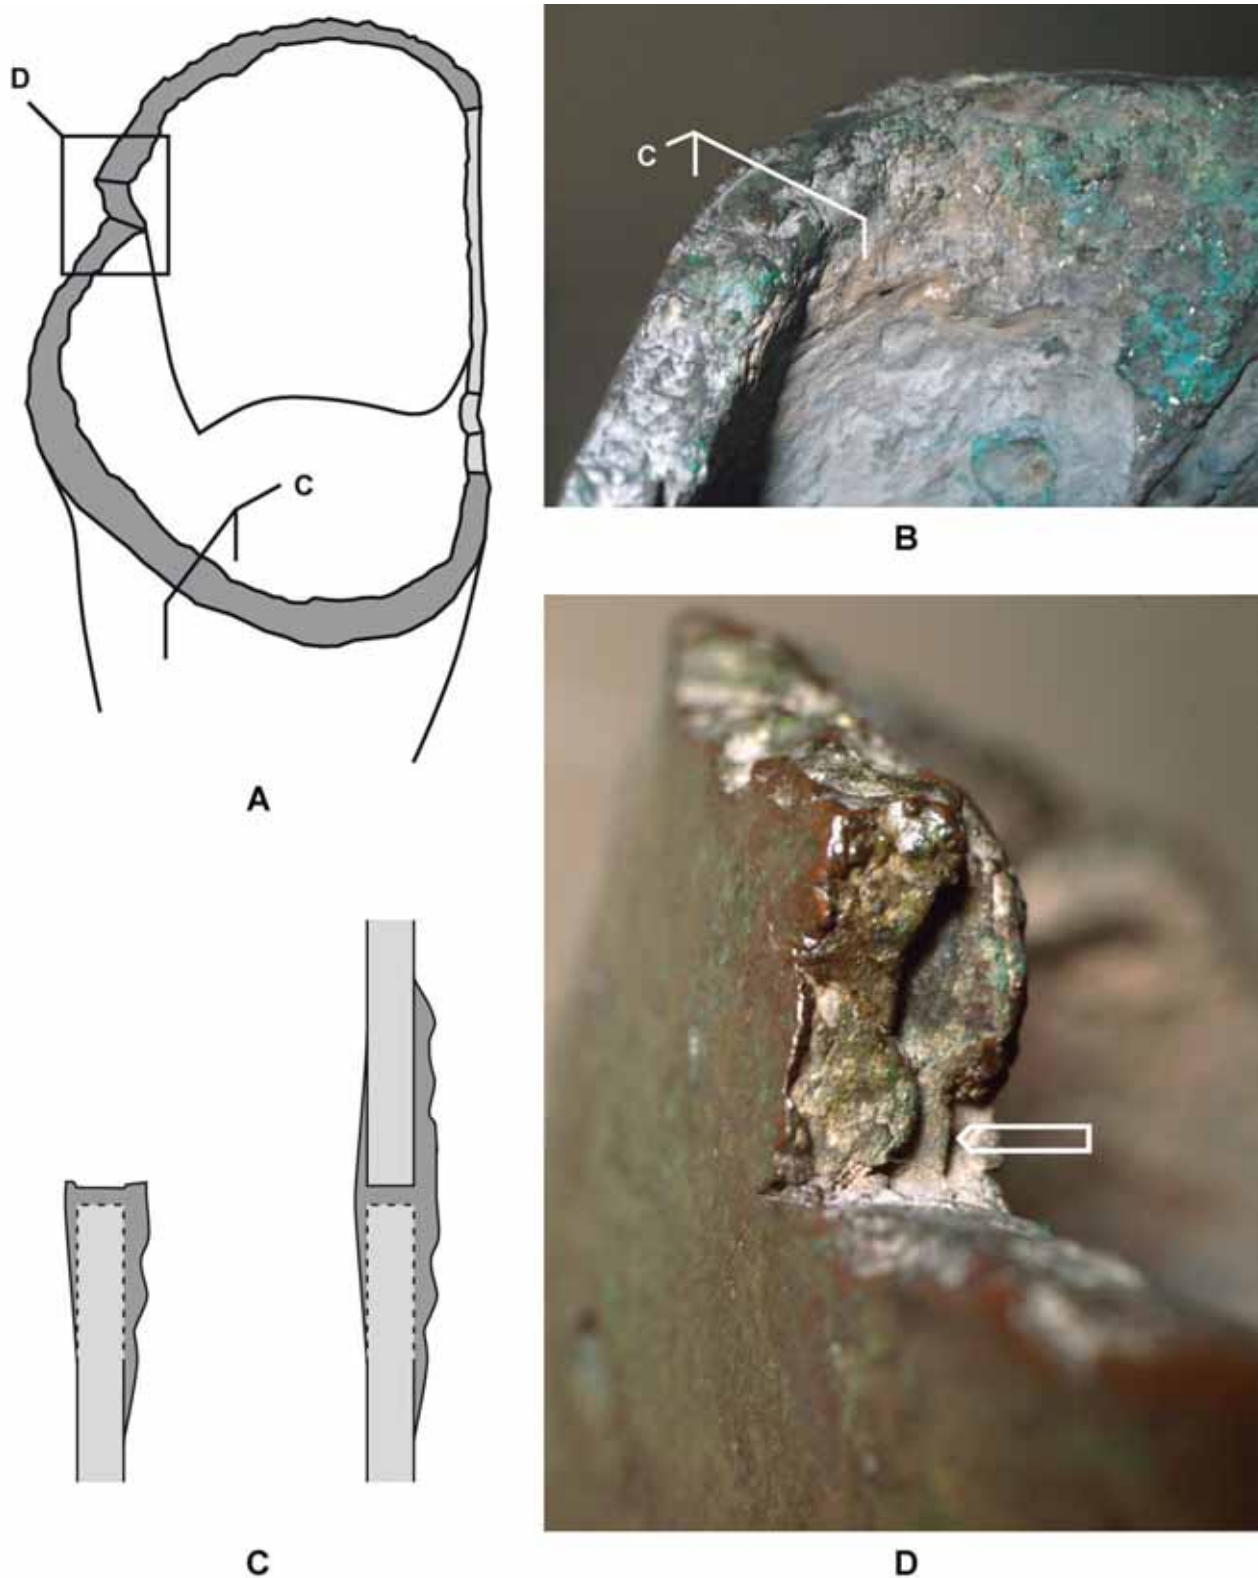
A : schéma de la soudure en cordon de la jambe de l'Apollon Chatsworth, localisation des zones recouvertes par le métal de soudure (gris foncé) ; la fracture entre la jambe-et le torse s'est produite exactement au niveau du cordon ; B, vue rapprochée du cordon de soudure, l'empreinte de la pièce supérieure (torse) est visible ; C, à gauche, schéma vu en section de la zone du cordon jambe-torse tel qu'il apparaît en B, à droite, restitution de l'assemblage avant la fracture ; le métal d'apport n'a probablement pas provoqué la fusion locale du bord inférieur du torse, et la fracture s'est produite à ce niveau. ; D, détail du ressaut, la flèche blanche désigne le seul emplacement où l'on peut apercevoir une portion du bord originel de la jambe tel qu'il a été préparé pour recevoir le métal de soudure.
